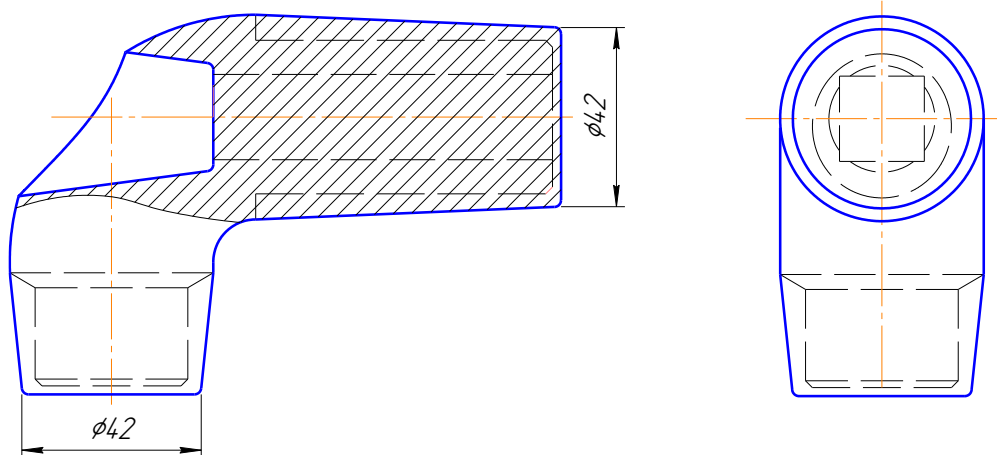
Конструкція заготовки деталі «Цапфа важелі»
